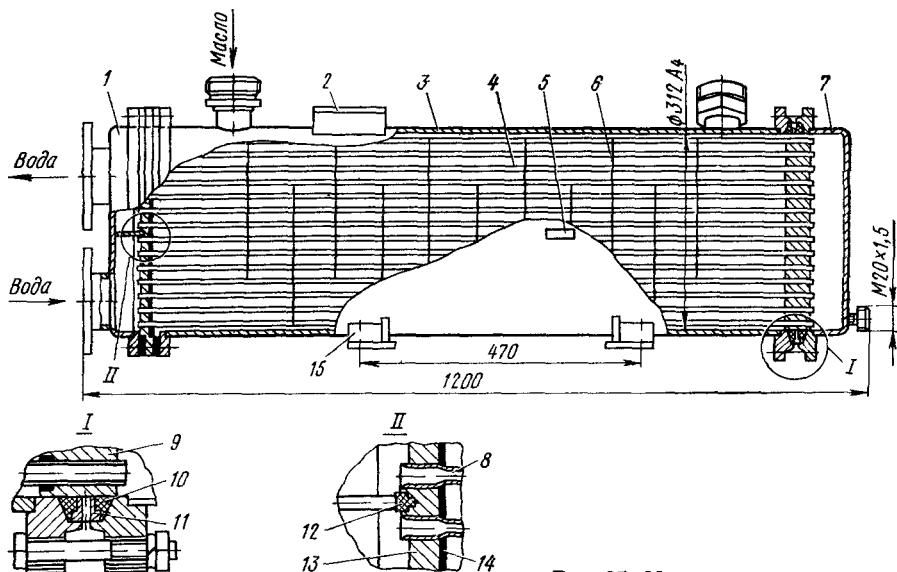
Маслоохладитель УГП: 1, 7 — крышки; 2 — табличка фирменная, 3 — корпус, 4 — охлаждающий элемент, 5 — ушко, 6 — перегородка; 8 — трубка, 9 — подвижная трубная доска, 10 — сальник, 11 — кольцо промежуточное, 12 — прокладка перегородки, 13 — неподвижная трубная доска; 14 — припой (ПОС-40), 15 — опора
